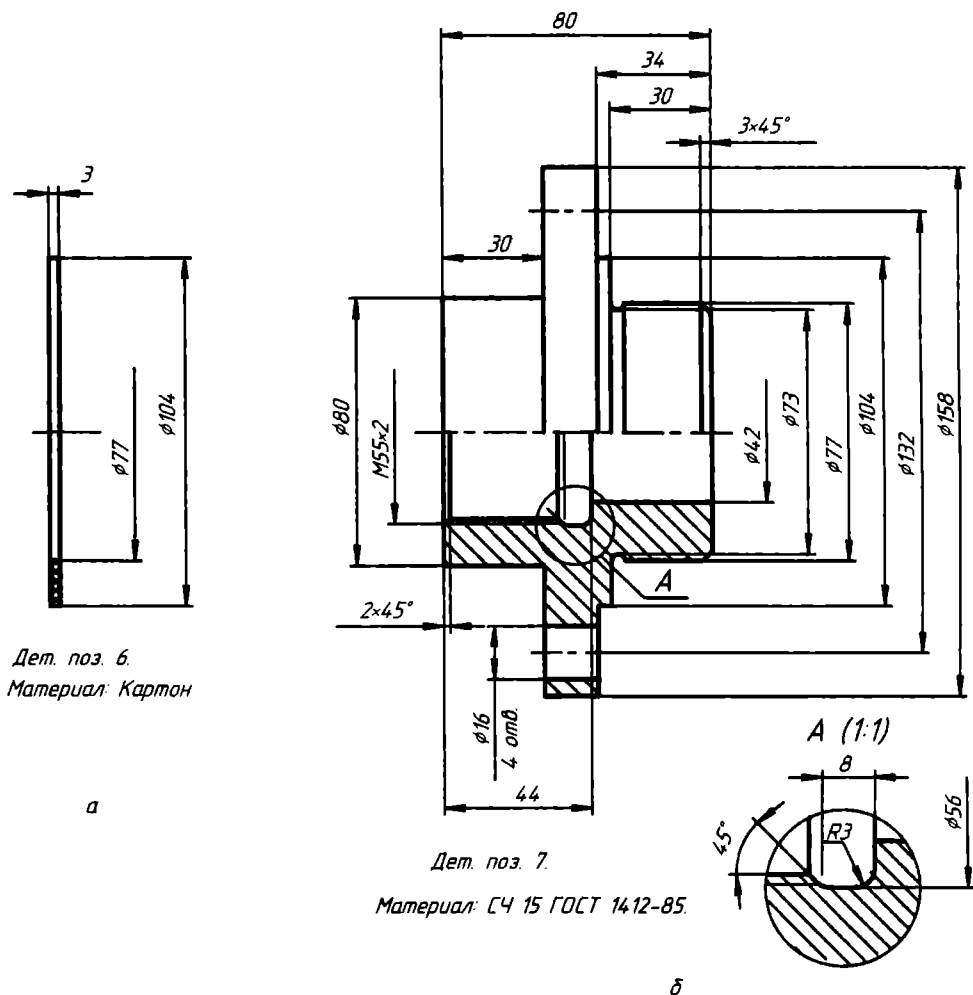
Чертежи: а — прокладки; б — крышки
